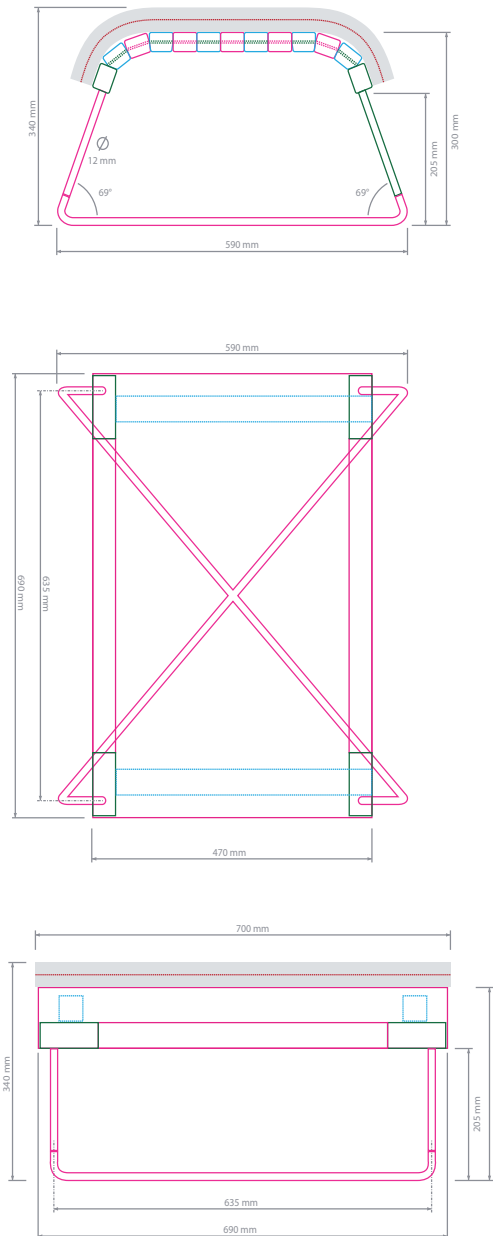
Konstrukční detaily - Fixace ohnutého tvaru v případě potřeby a detaily utahovacího dílu s pásem
